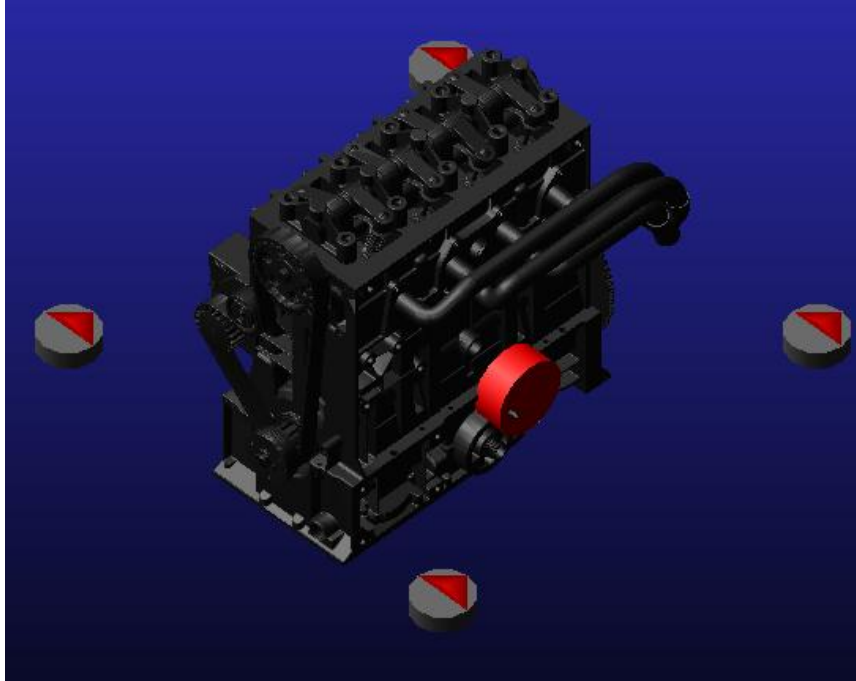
Motor de 4 cilindro en línea exportado a Adams Car
